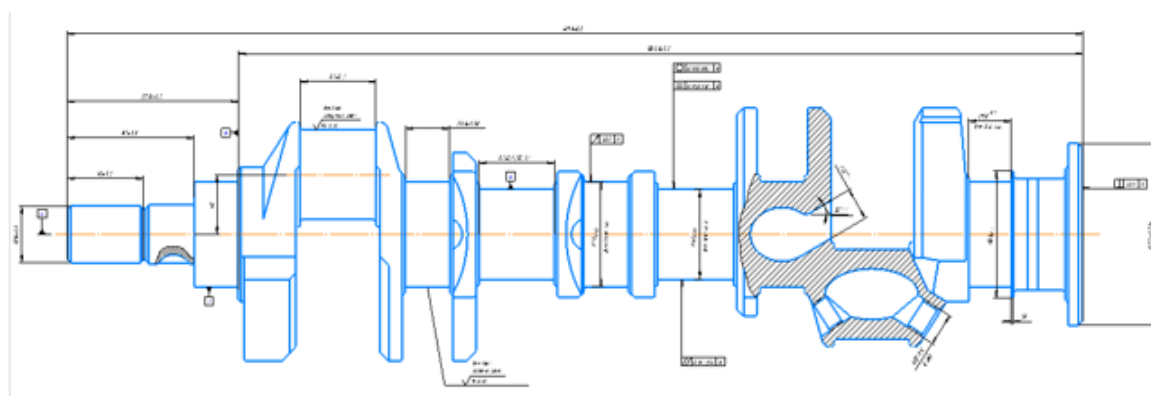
Коленчатый вал двигателя ЗМЗ-511
